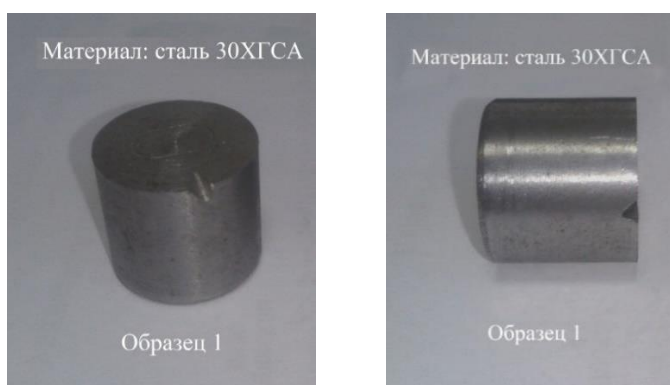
Внешний вид образцов из стали 30ХГСА после годовой выдержки на воздухе, при T=23-25 С
